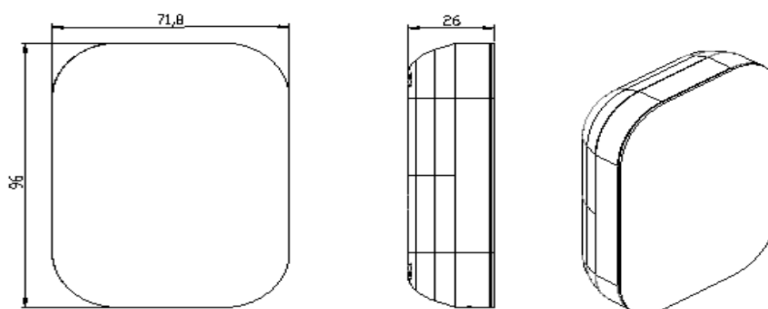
Dimensioni meccaniche Sensore ON/OFF
